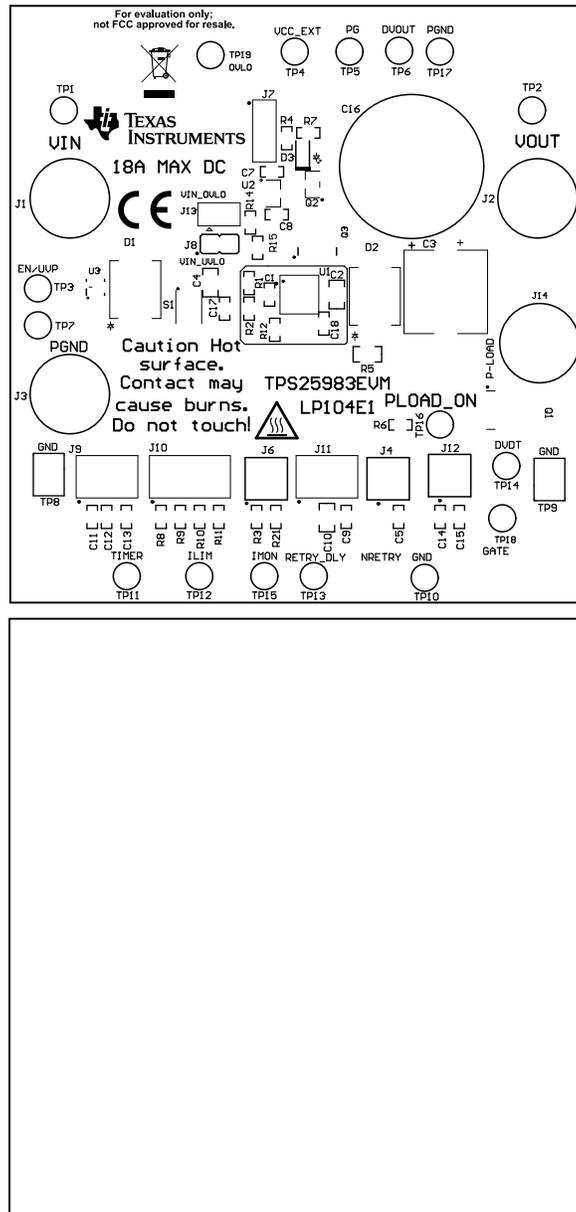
TPS25983EVM 电路板 (a) 顶层装配图 (b) 底层装配图
